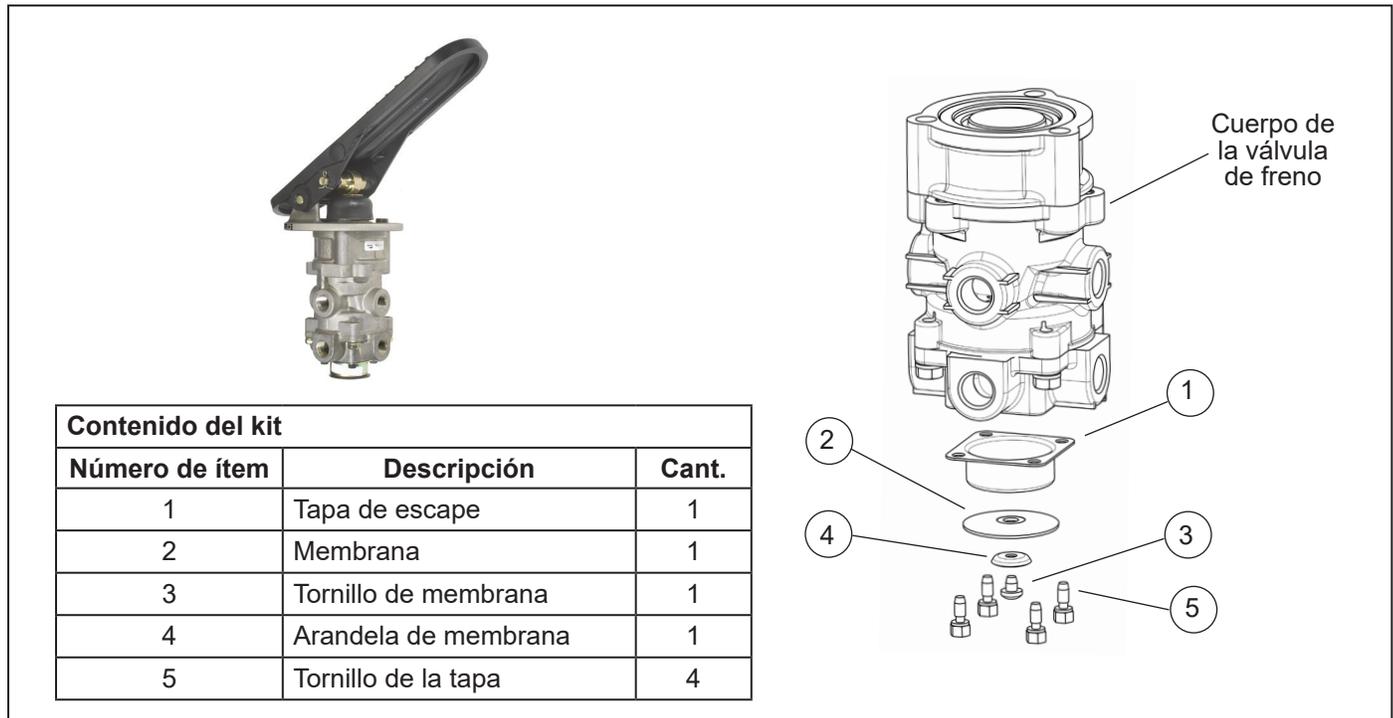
Bendix® E-10™ Kit de la tapa de escape de la válvula de freno
